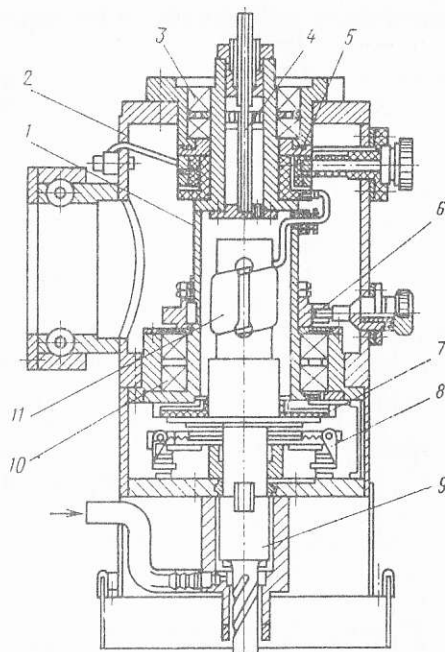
Приспособление для электрохимико-ультразвукового шлифования
